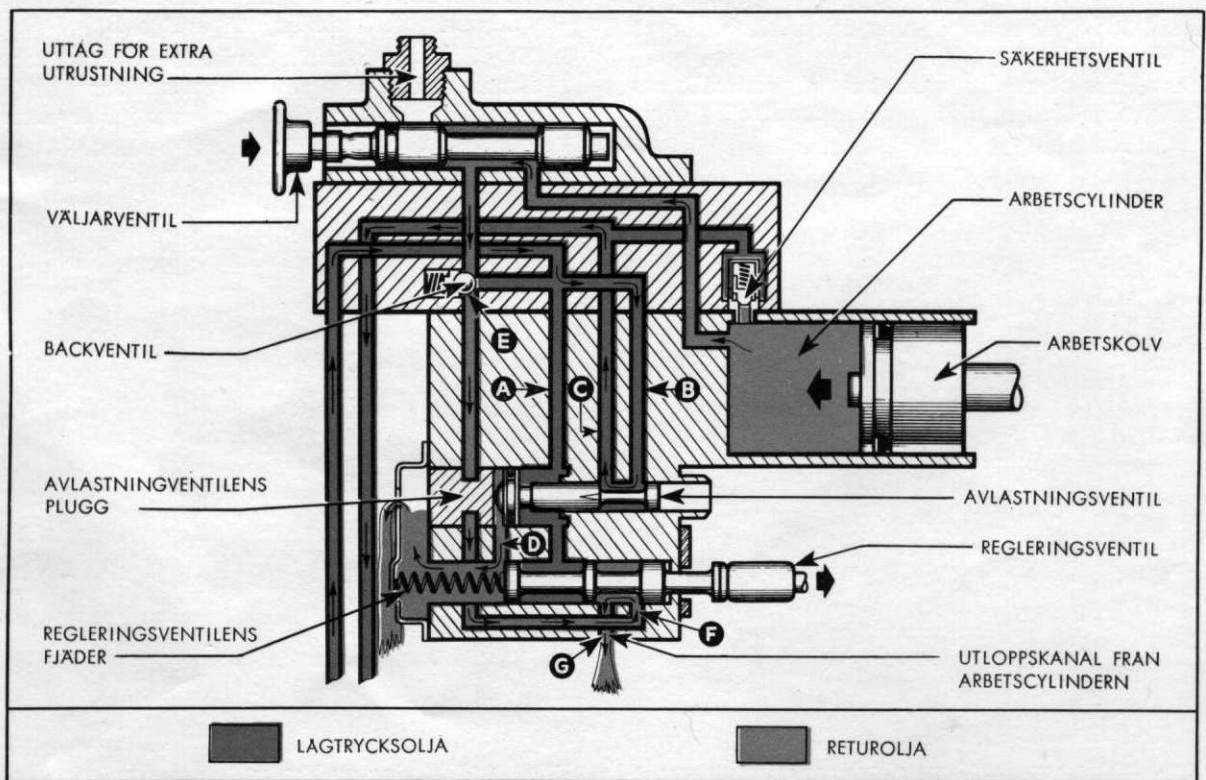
Hydrauliska systemets oljeflöde — sänkning.
